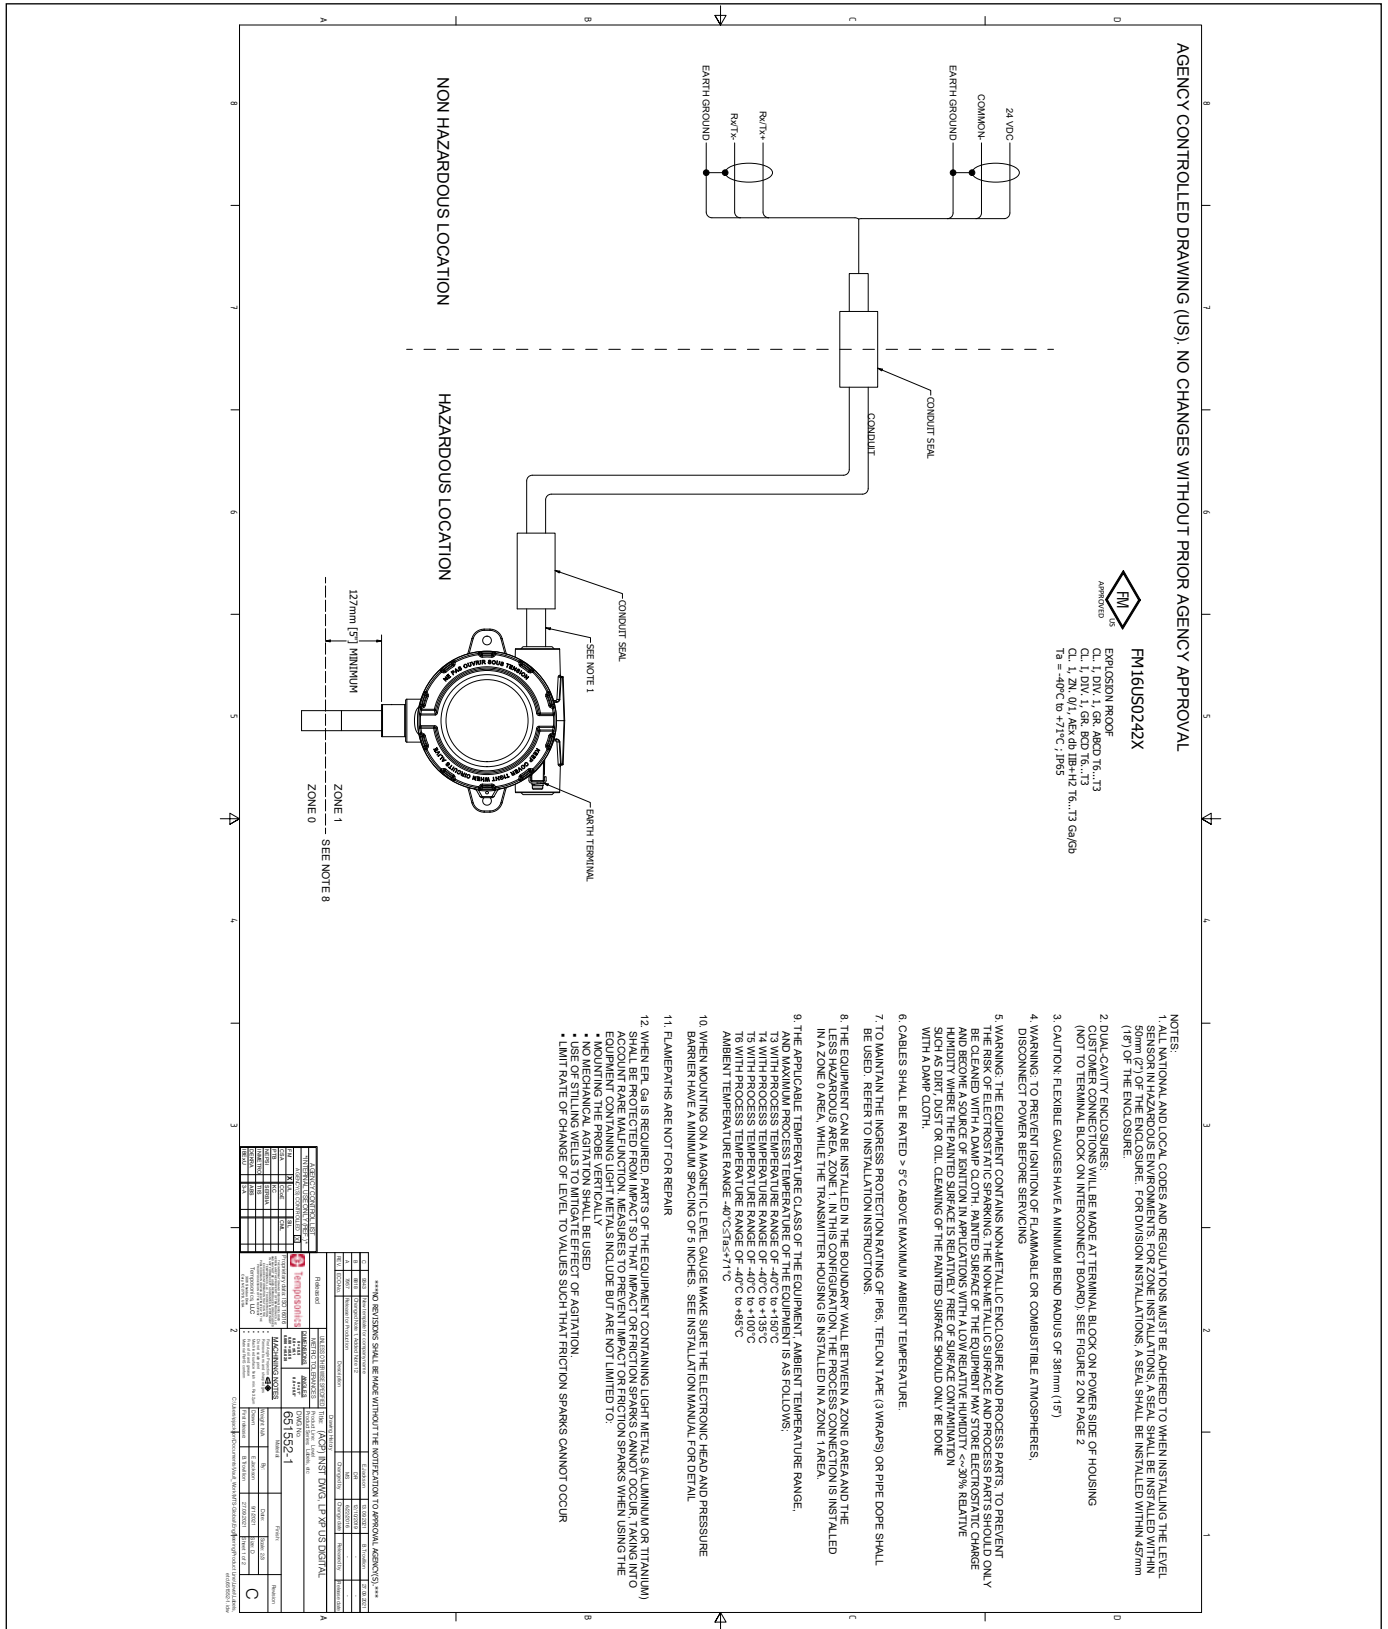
Explosionsgeschützt, FM-Montagezeichnung, Modbus und DDA, Seite 1
